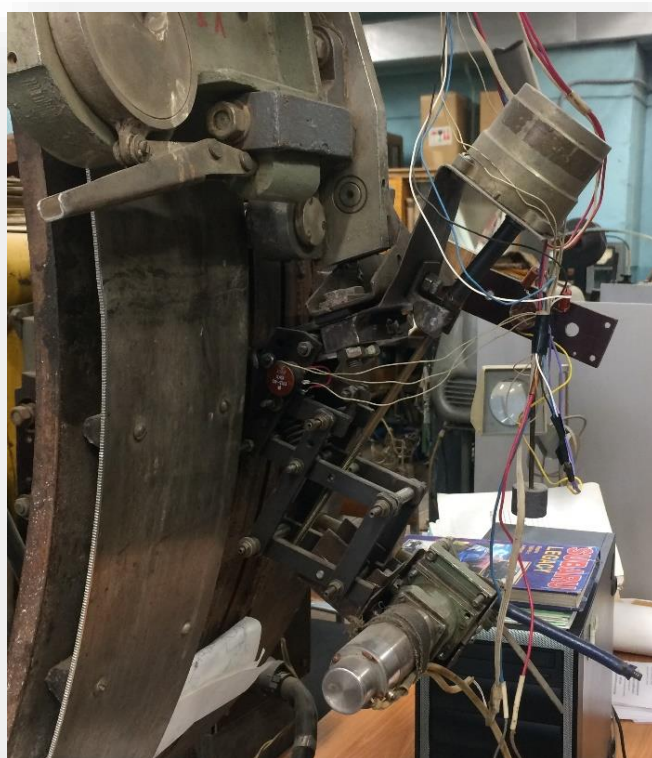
макет (механизм корректировки угла наклона сварочной головки).
